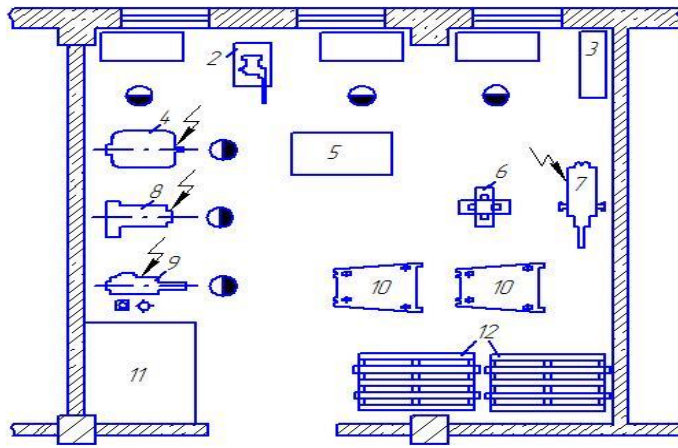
Технологічне планування бляхарського відділення: 1 – верстаки; 2 – ножиці; 3 – стелаж; 4 – станок вертикально-свердлильний; 5 – плита рівняльна; 6 – стенд для ручного рихтування; 7 – станок шліфовальний; 8 - зиг-машина; 9 – установка для зварювання; 10 – візок-стенд для ремонту кабін; 11 – місце для зберігання листового матеріалу; 12 – стелажі для крил.
